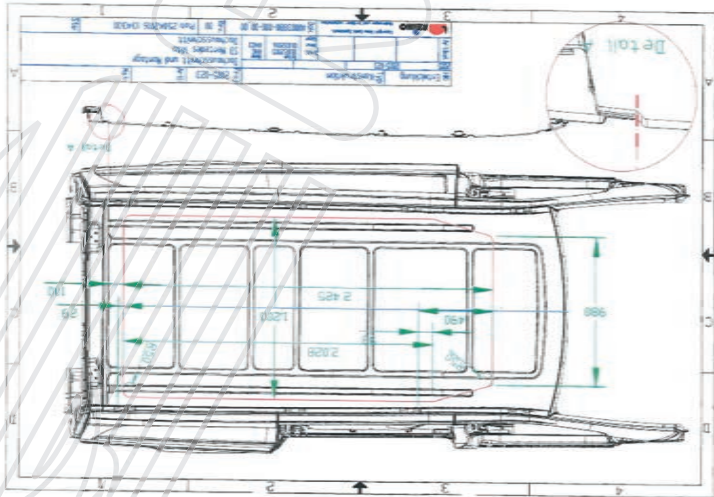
Zeichnung Dachausschnitt 3
